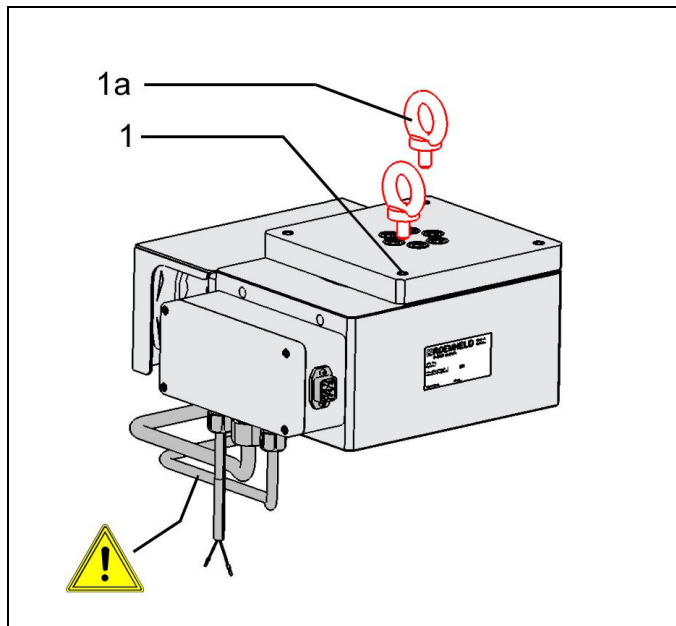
Punto per il sollevamento tramite carrello elevatore a forca (versione verticale 6509 1036 E)
